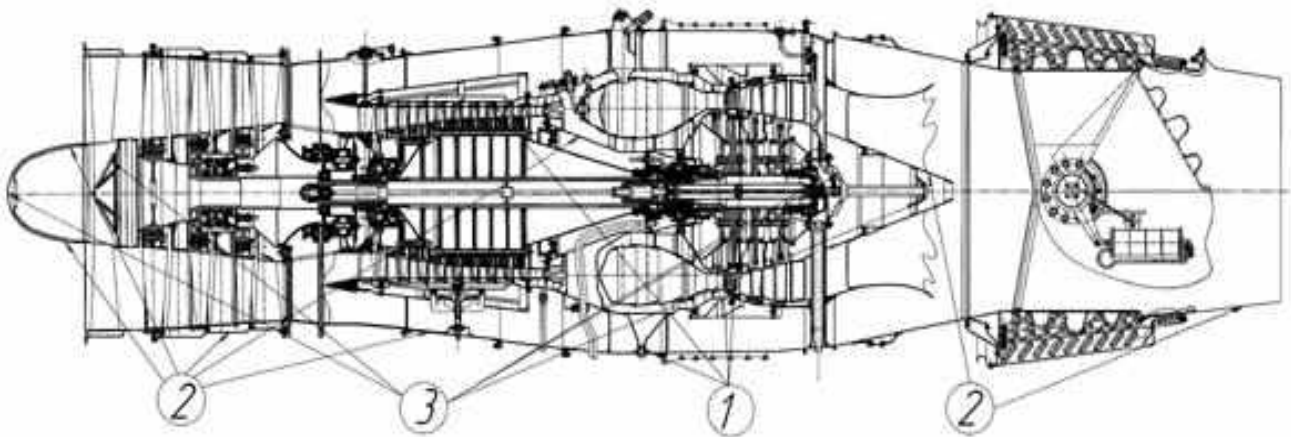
Класифікація деталей двигуна і форм заготовок для виготовлення штампуванням вибухом:
